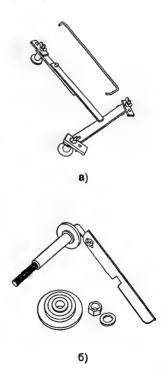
Специальный инструмент: а — съемник переднего фланца барабана; б — приспособление для демонтажа подшипников и сальника
